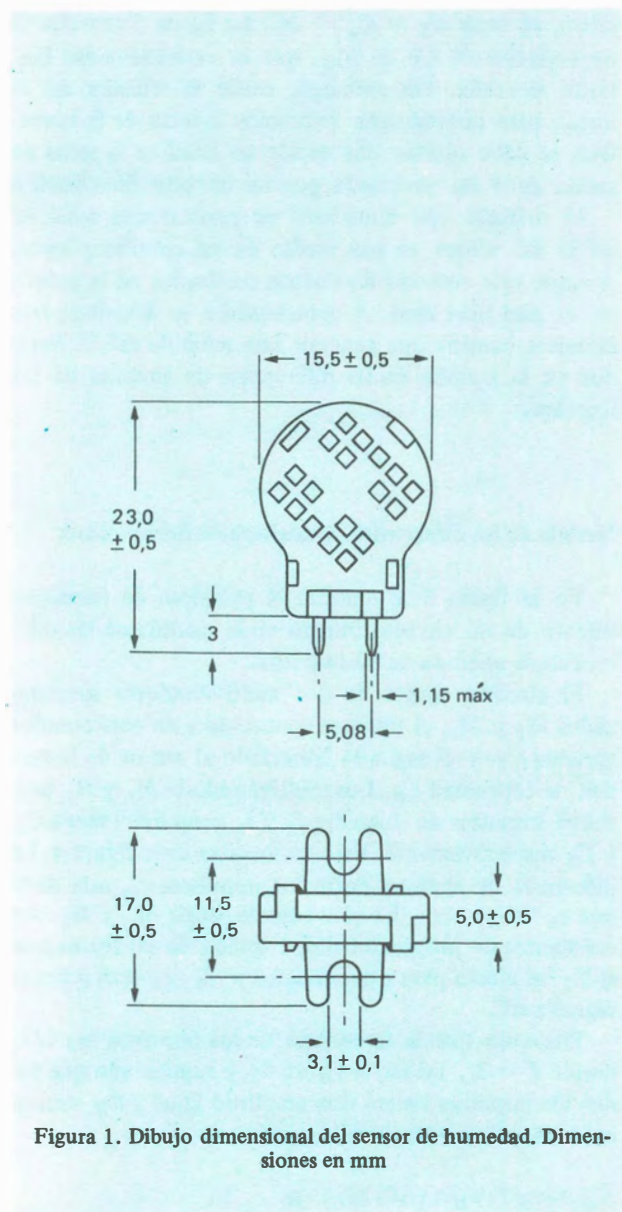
Dibujo dimensional del sensor de humedad. Dimensiones en mm
